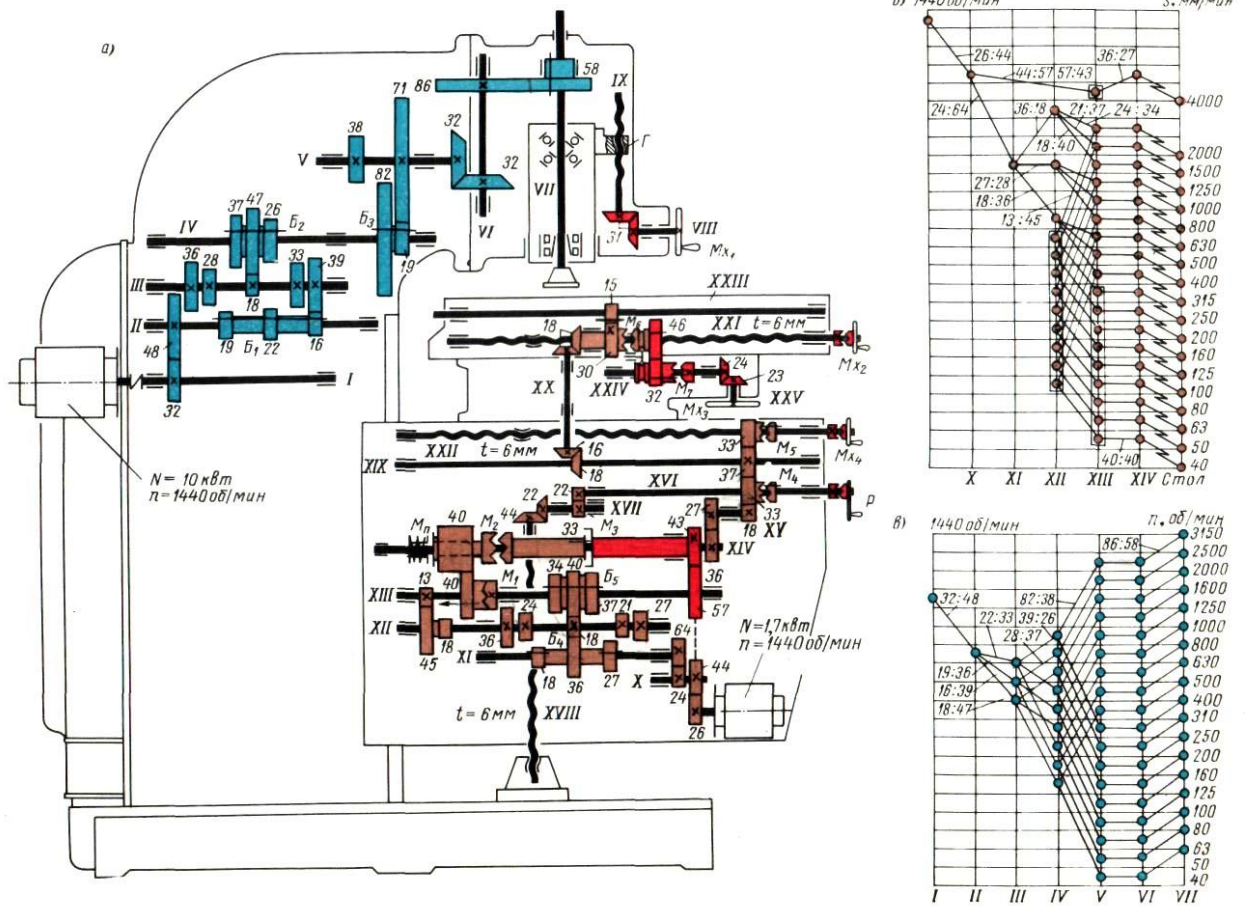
Кинематическая схема горизонтально-фрезерного станка
